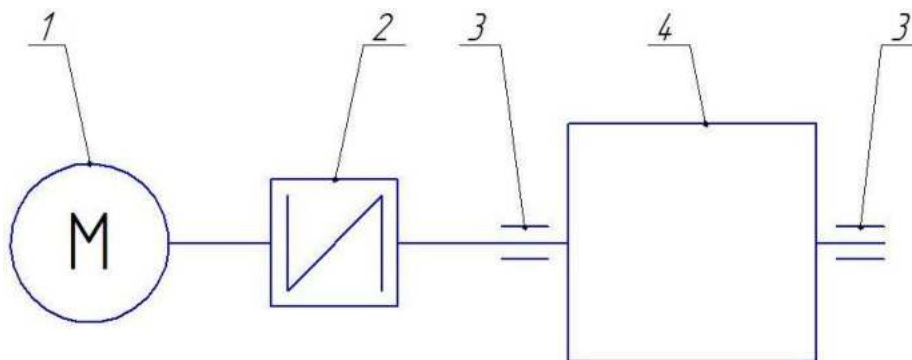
Кинематическая схема модернизированного привода галтовочного барабана:
